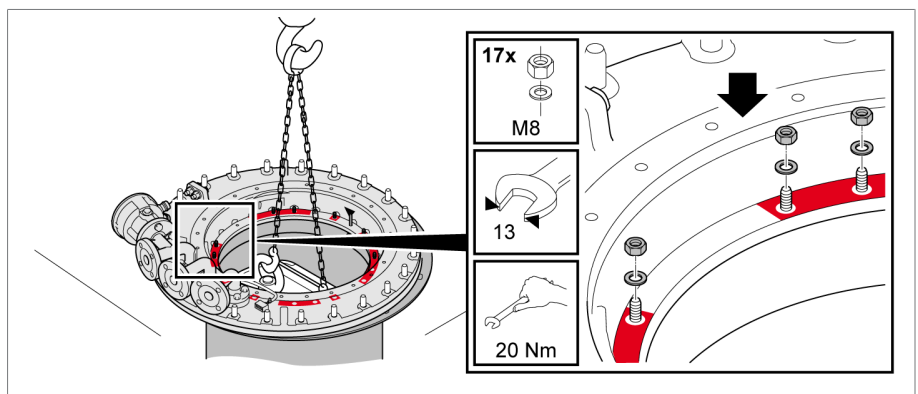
Laststufenschalterkopf mit Stützflansch verschrauben
